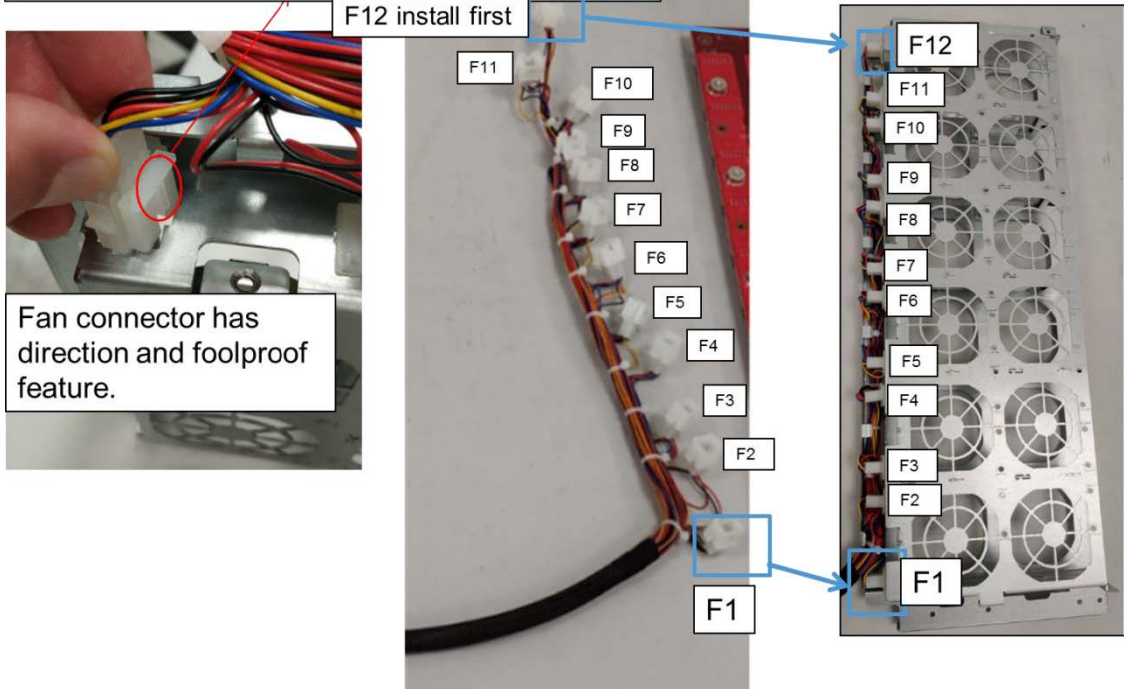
Ensamblaje del cable del ventilador al soporte del ventilador
